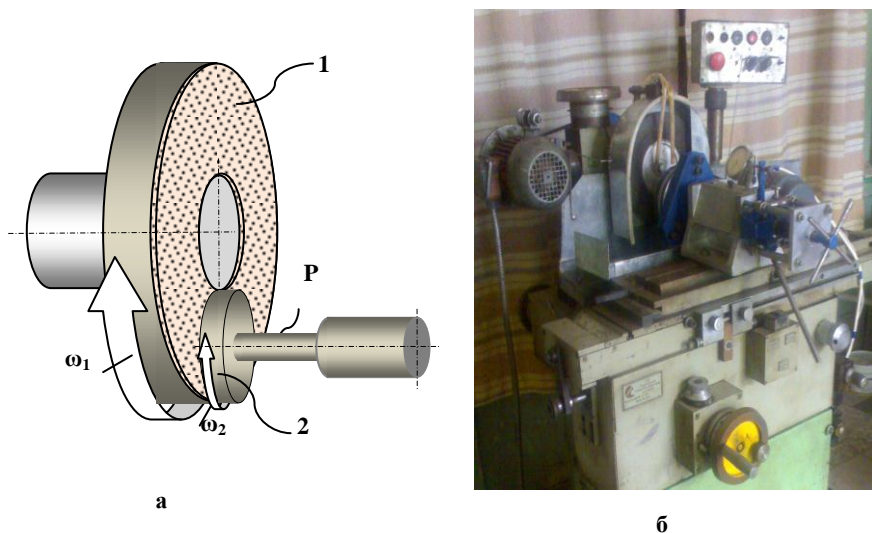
а - Схема НПСШ: 1- шлифовальный круг, 2- кассета с деталями; б - лабораторная установка для НПСШ
